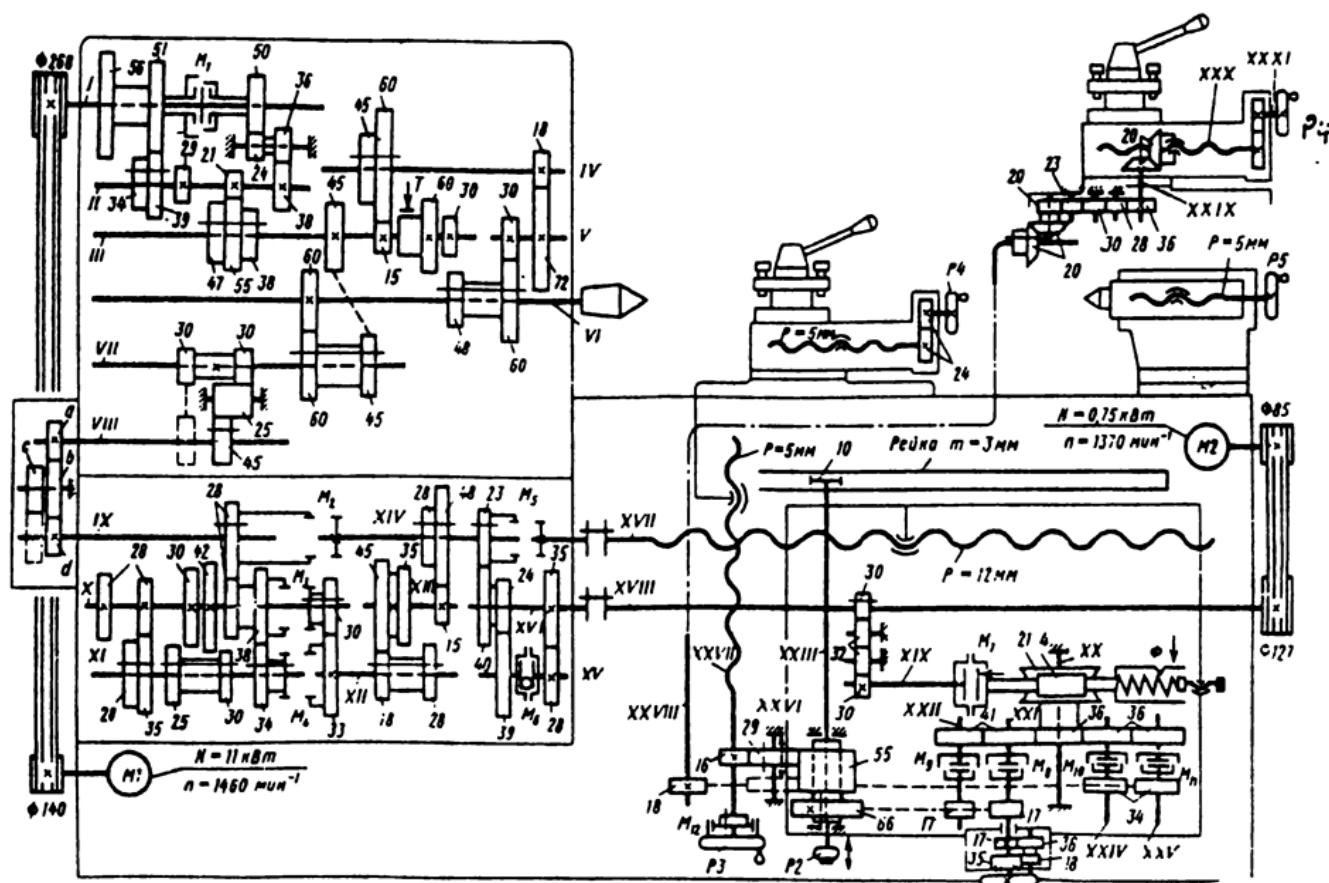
Кинематическая схема токарно-винторезного станка 16К20
